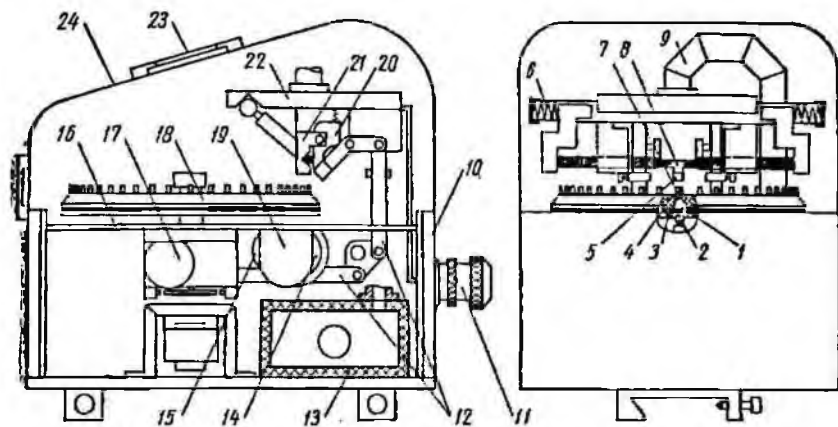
Конструкция автоматической установки АПС-ПВ-40.
